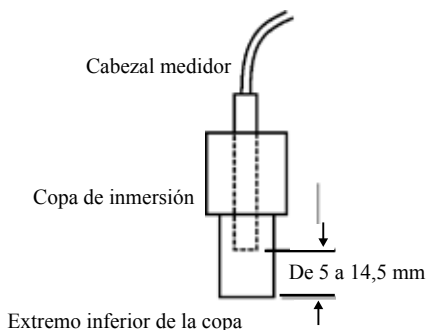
Montaje del cabezal medidor con copa de inmersión
